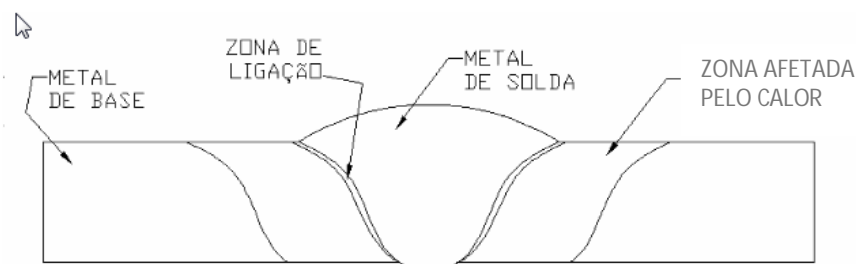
Desenho esquemático mostrando a ZAC, numa junta soldada [21].
